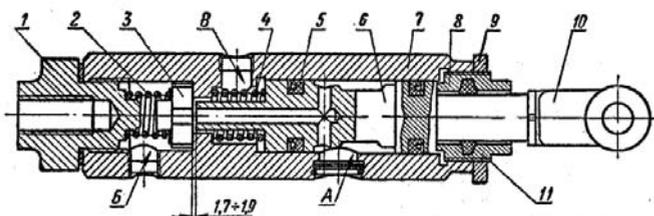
Следящее устройство: 1 — переходная гайка; 2, 4 — пружина; 3 — клапан; 5 — манжета; 6 — плунжер; 7 — корпус; 8 — регулировочная гайка; 9 — контргайка; 10 — вилка; 11 — войлочное кольцо, А — отверстие, соединенное с атмосферой; Б — отверстие, соединенное с пневмосистемой; В — отверстие, соединенное с пневмокамерой
